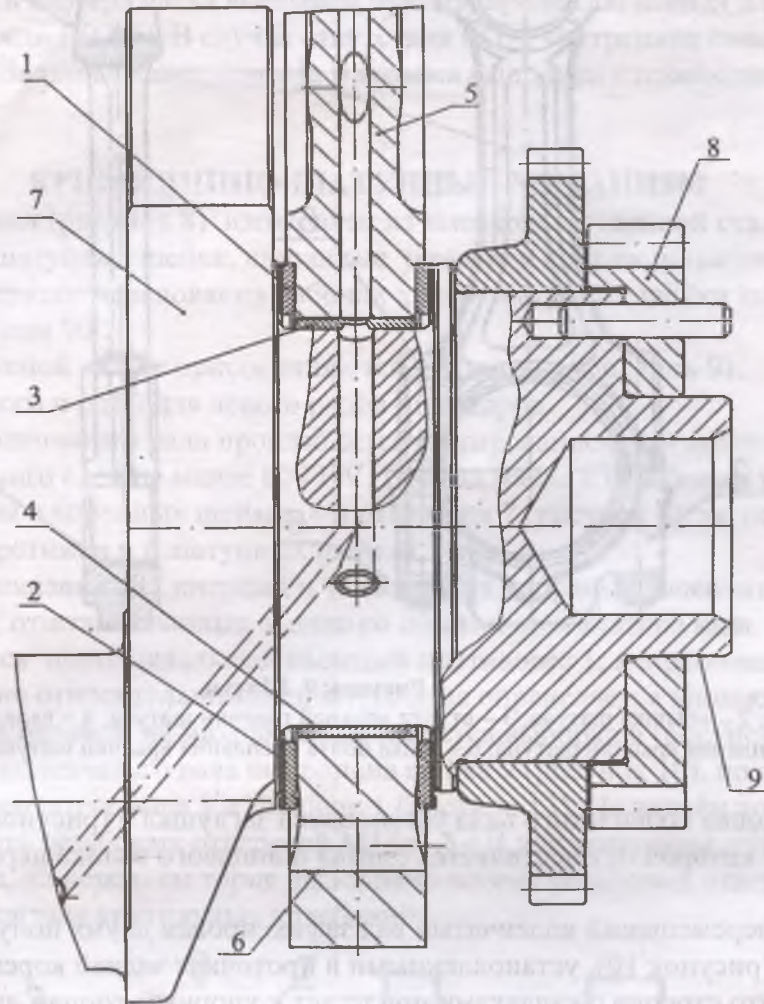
Установка упорных полуколец и вкладышей коленчатого вала
